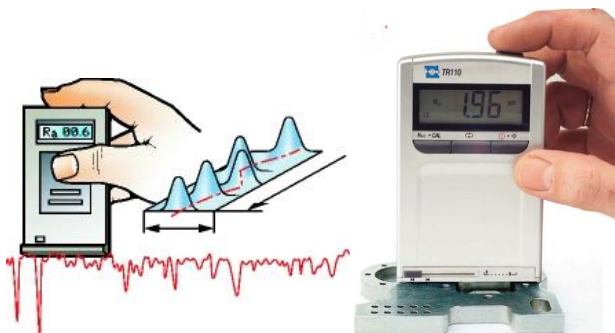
Портативный измеритель шероховатости наружной поверхности (профилометр).
